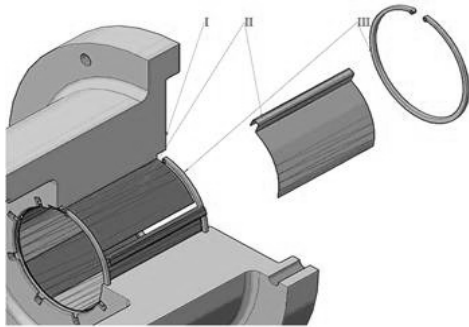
Лепестковый опорный газодинамический подшипник
